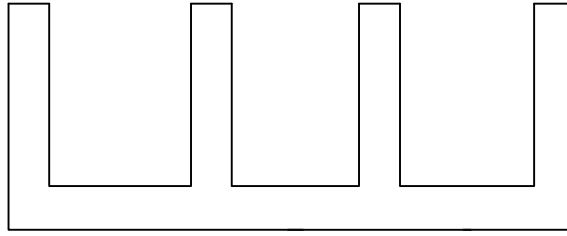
Corte transversal del bloque para el cálculo del volumen
